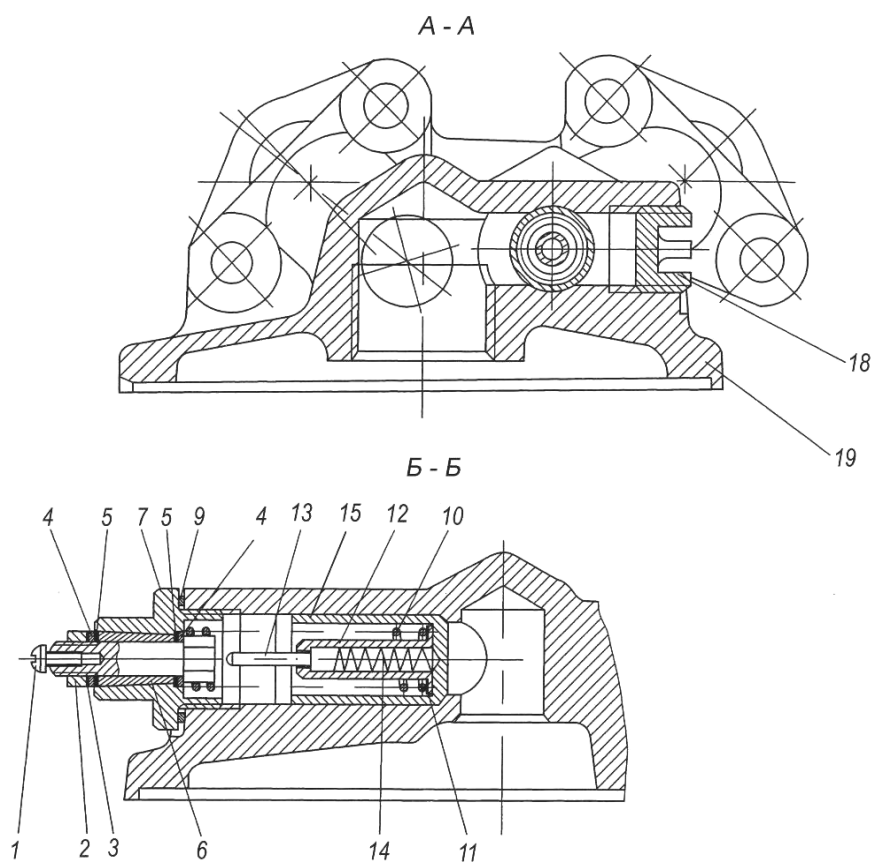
Корпус масляного фильтра в сборе
